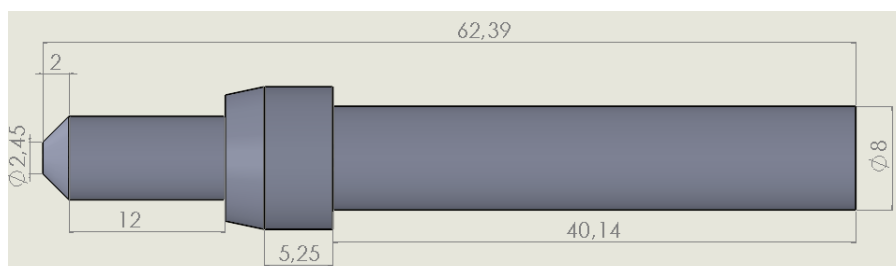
Cuarto diseño de fixture guía realizado en solidworks.
